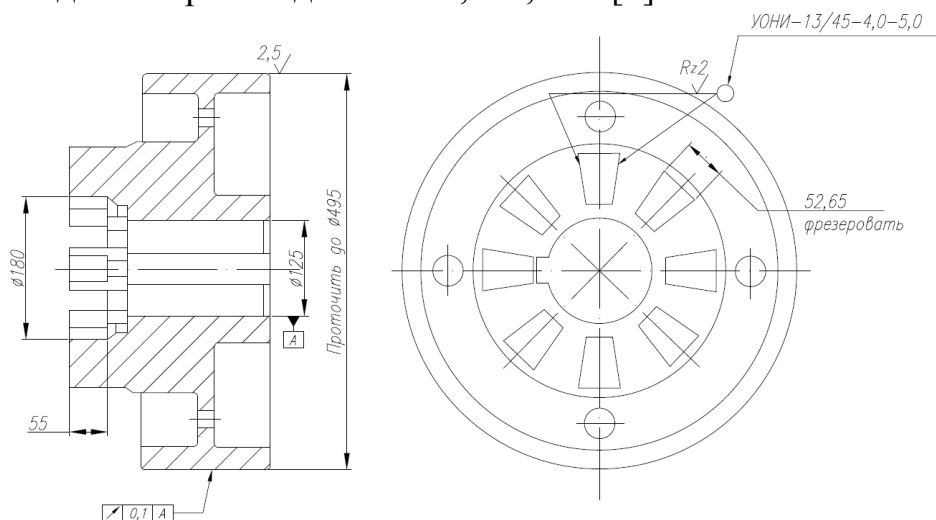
Ремонтный чертеж тормозного шкива-полумуфты
